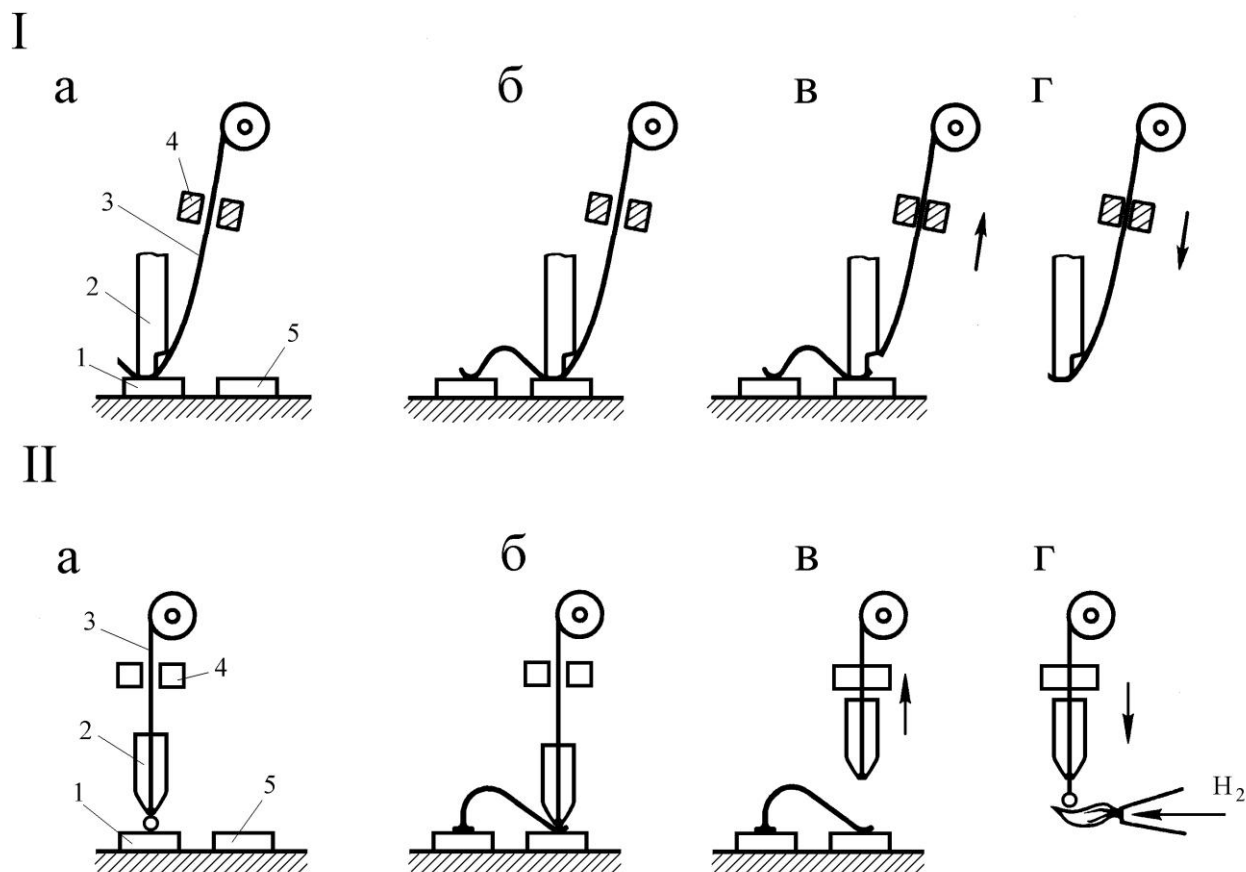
Варианты выполнения сварки термокомпрессией: без оплавления проволоки (I) и с оплавлением (II): а – первая сварка; б – вторая сварка; в – обрыв проволоки; г – подготовка проволоки к следующей сварке: 1 – контактная площадка кристалла; 2 – сварочный инструмент; 3 – проволока; 4 – зажим; 5 – контактная площадка на монтируемой подложке (или вывод корпуса)
